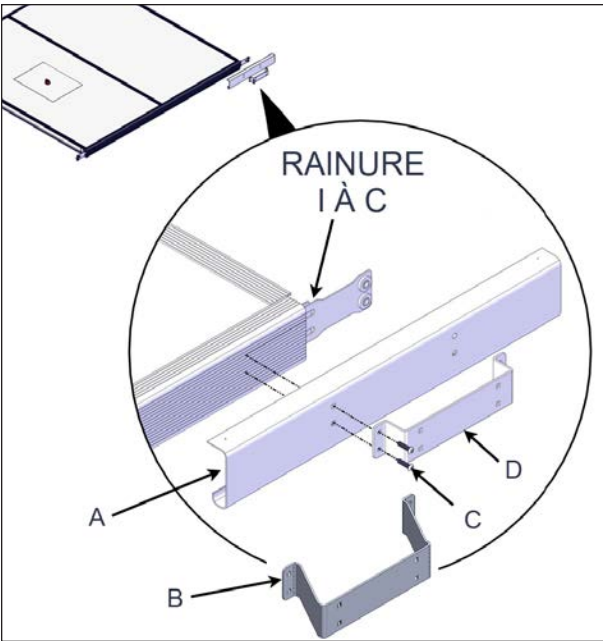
INSTALLATION DES SUPPORTS DE MONTAGE
